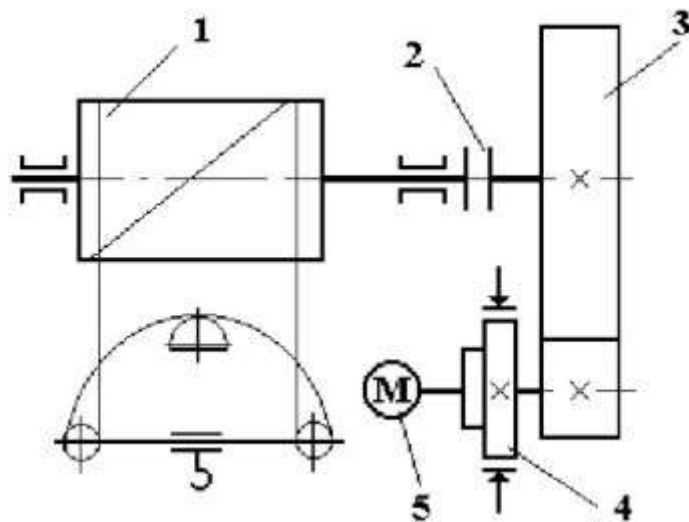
Кінематична схема механізму підйому: 1 - барабан; 2 - муфта; 3 - редуктор; 4 - гальмо; 5 - електродвигун
